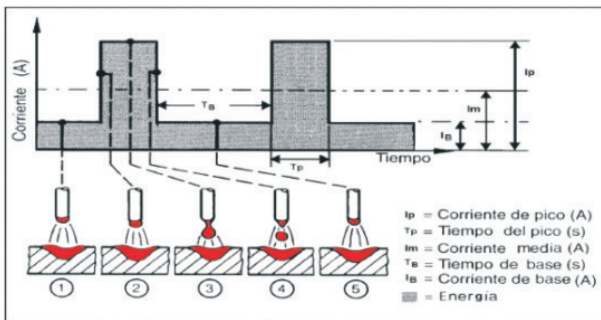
Parámetros típicos de la soldadura GMAW-Pulsada.
